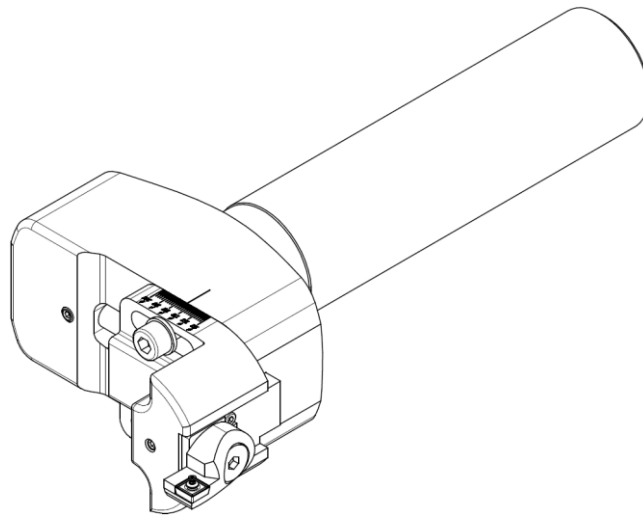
Загальний вигляд головки розточної збірної
